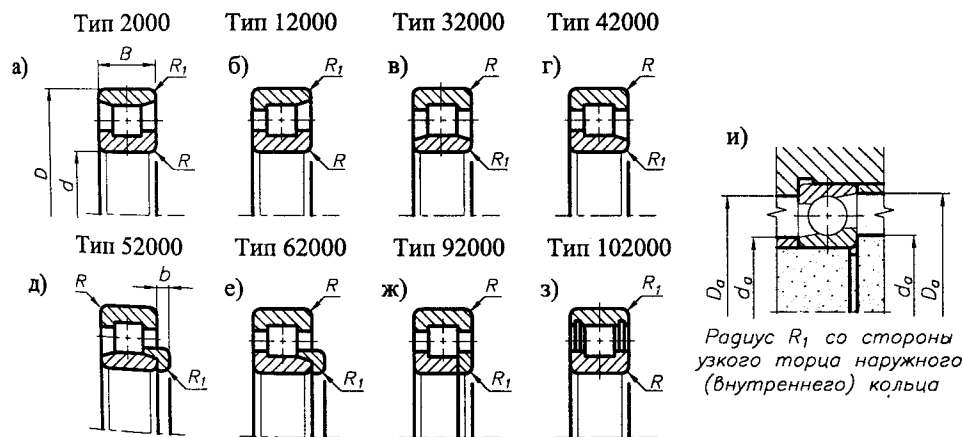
Габаритные и установочные размеры роликовых радиальных с короткими цилиндрическими роликами подшипников
